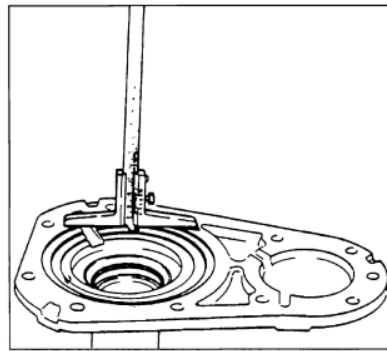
Вимірювання глибини гнізда під роликпідшипник первинного вала.
